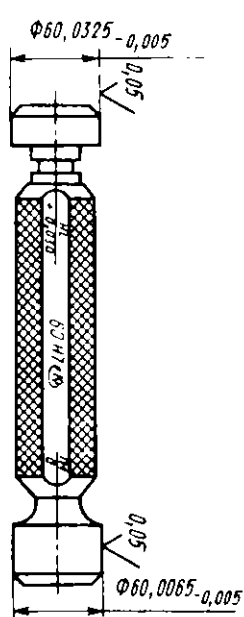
Двусторонний двухпредельный калибр-пробка
